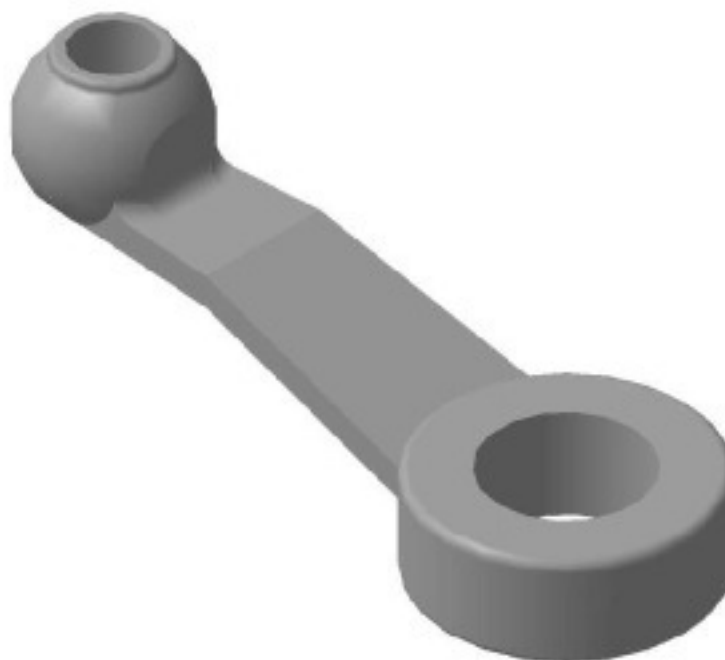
3D-модель заготовки виготовленої литтям в оболонкові форми
